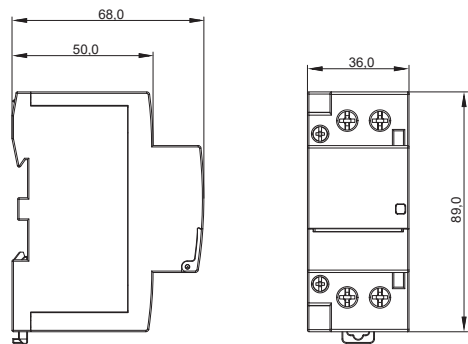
Габаритные размеры контакторов от 40 А до 63 А, 2P / Figure 3 – Overall dimensions of contactors from 40 A to 63 A, 2P
